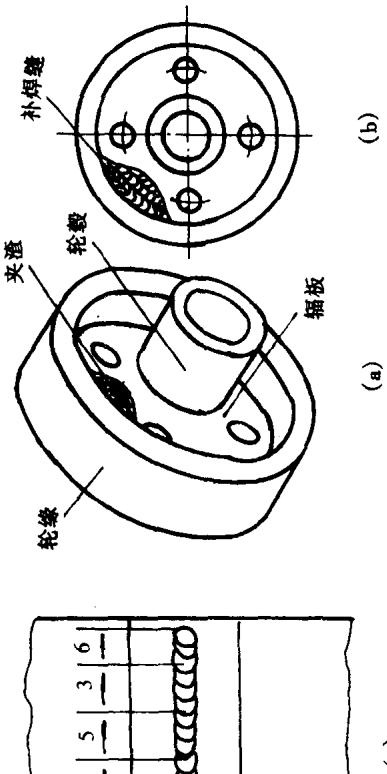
齿轮毛坯夹渣热焊法焊补
